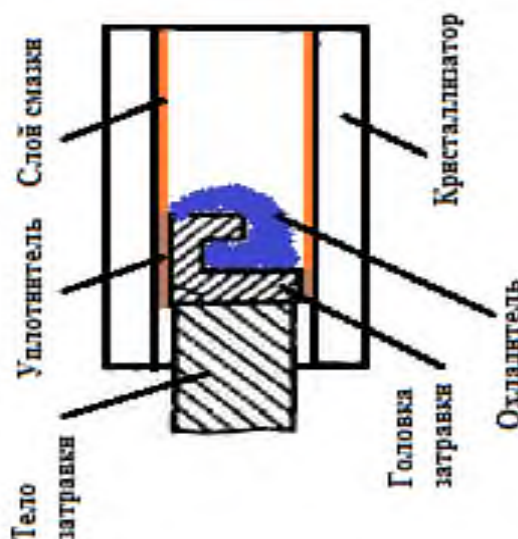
Схема подготовки кристаллизатора МНЛЗ к разливке
